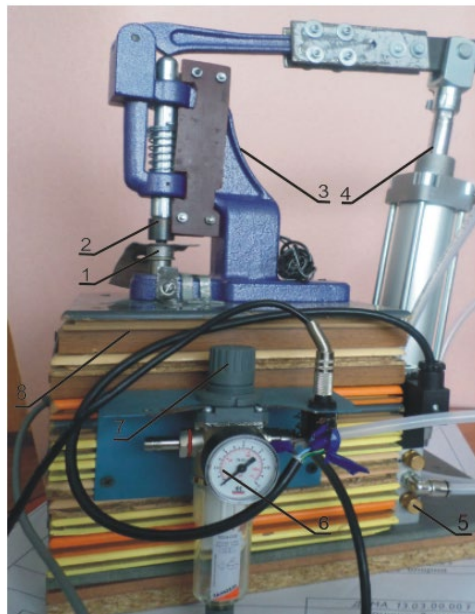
Установка для дослідження процесу встановлення металевих люверсів у виробках легкої промисловості: 1-матриця; 2- пуансон; 3- ручний механічний прес;4- пневматичний циліндр; 5- пневматичний розподільник; 6 – манометр, 7- регулятор тиску; 8- основа
